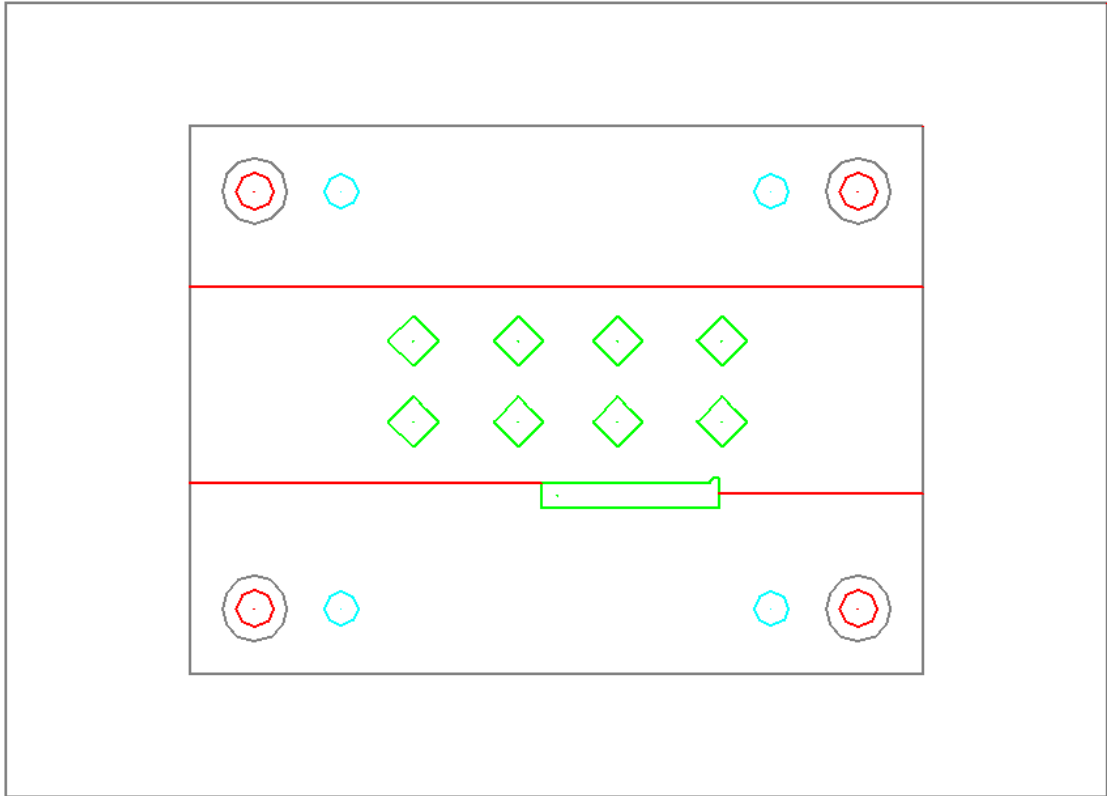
Kesme kalıbındaki dişi çeliğin gösterilmesi
